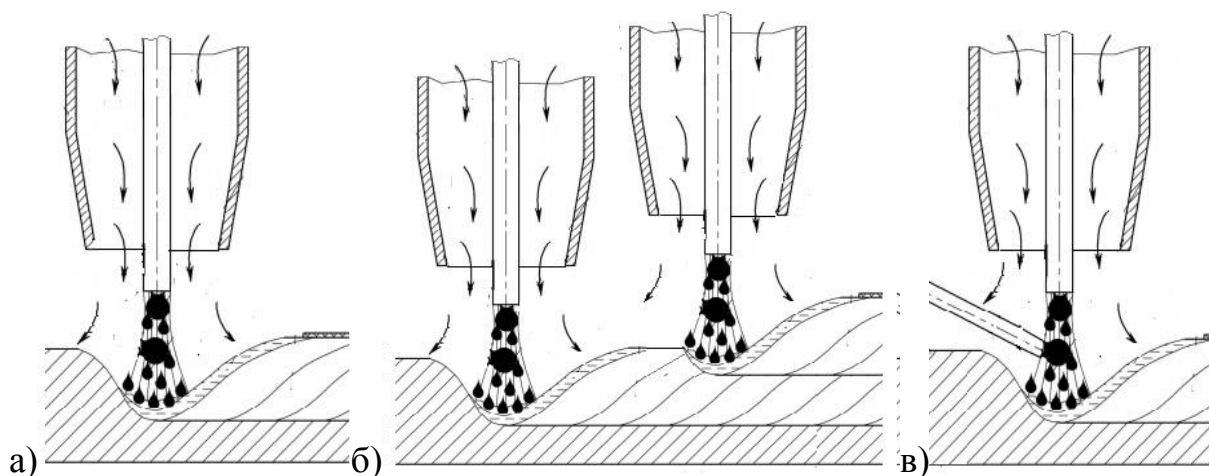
Варианты сварки плавящимся электродом в защитных газах: а) классическая однодуговая сварка; б) двухдуговая сварка; в) сварка с дополнительной присадочной проволокой
